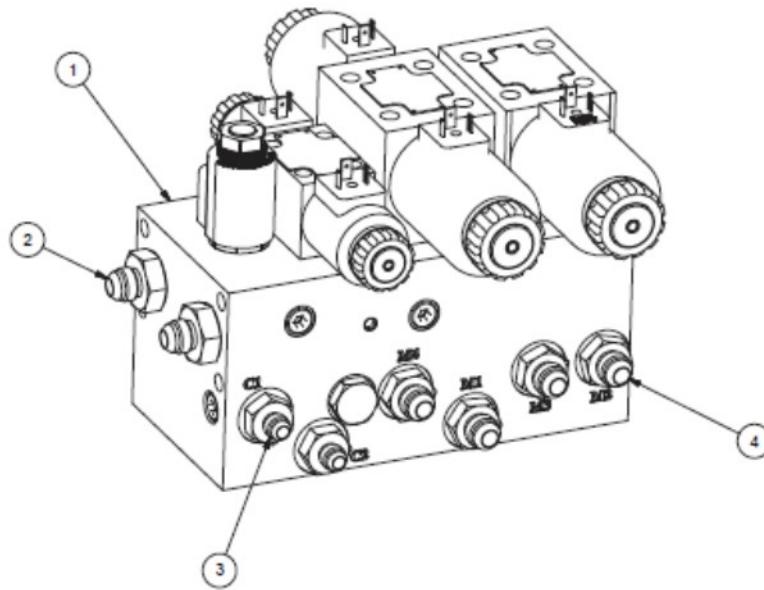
Чертеж узла – группа клапанов – 815846
